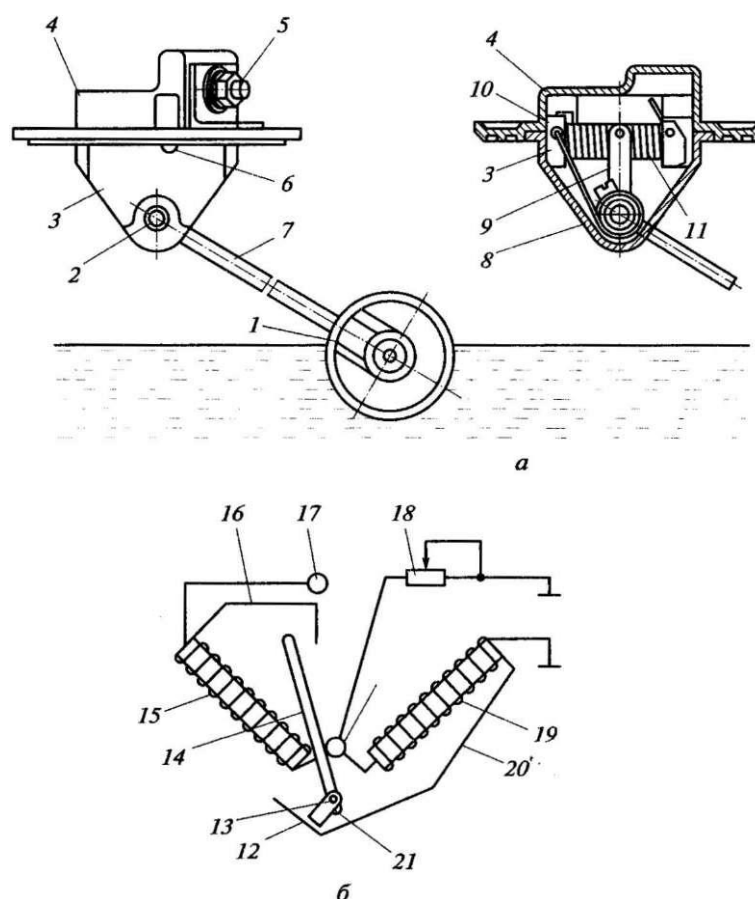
Электромагнитный указатель уровня топлива: а — датчик; б — схема указателя; 1 — поплавок; 2 — ось ползунка реостата; 3 — нижняя часть корпуса; 4 — верхняя часть корпуса; 5 — выводной контакт; 6 — винт крепления; 7 — рычаг поплавка; 8 — проволоочная петля; 9 — подвижный контакт (ползунок) реостата; 10 — пластина реостата; 11 — обмотка реостата; 12, 16, 20 — полюсный наконечник указателя; 13 — противовес стрелки указателя; 14 — стрелка указателя; 15, 19 — обмотки указателя; 17 — входной контакт питающего напряжения; 18 — реостат; 21 — якорек; 22 — контактный зажим
